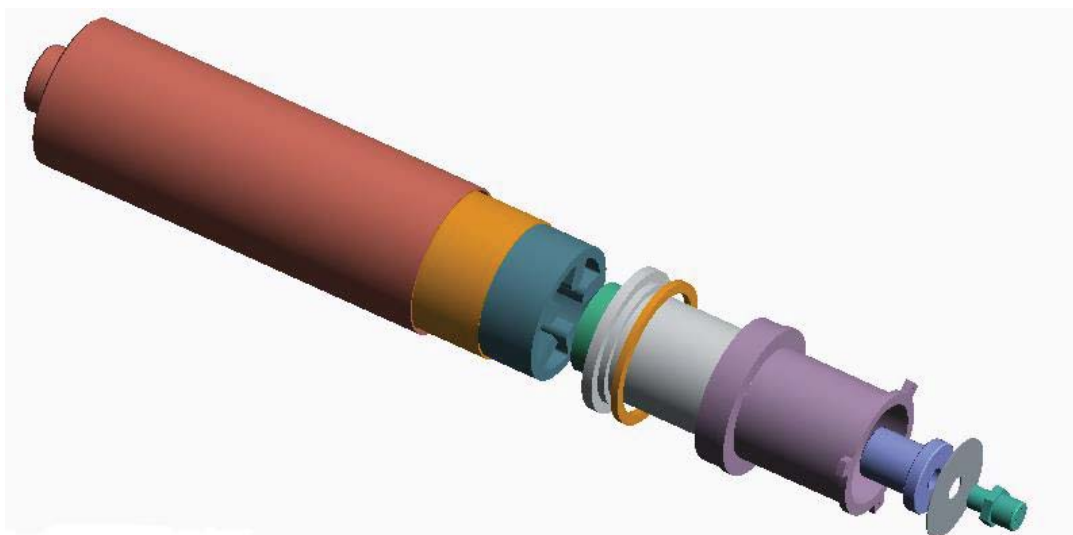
Разнесённый вид 3D-модели РДТТ 755 NsMotor
